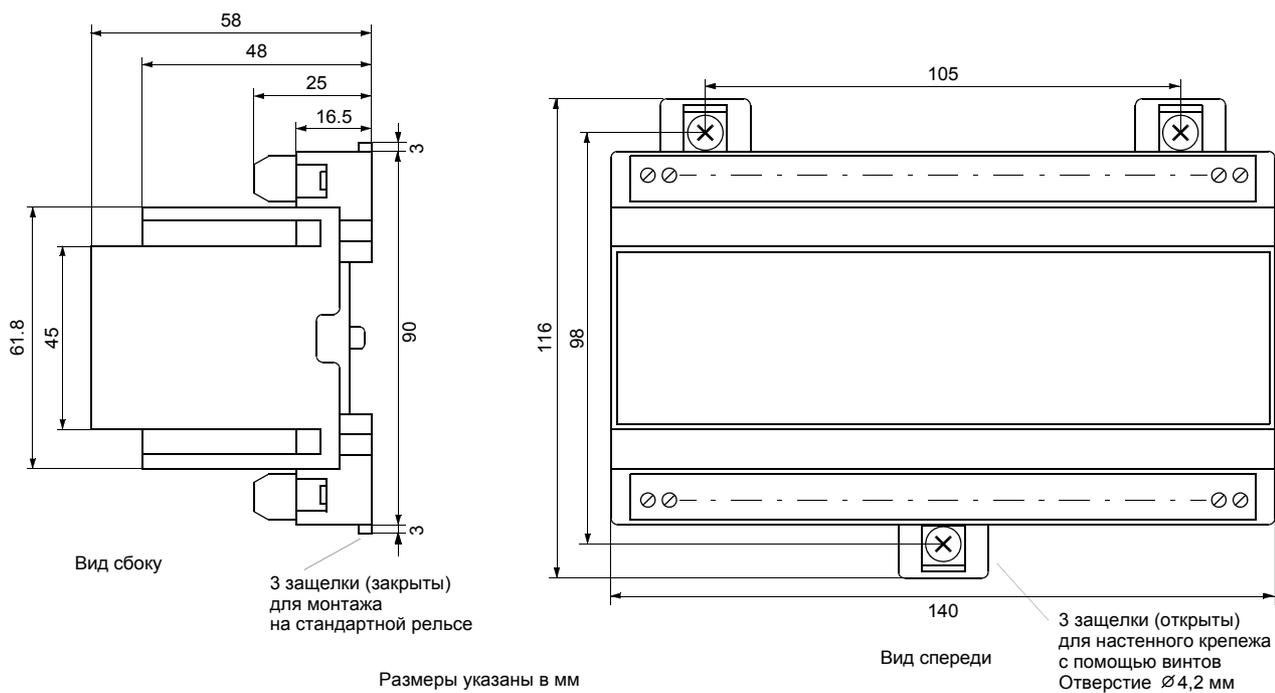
Размеры термодатчика 7XV5662-*AD10-0000
